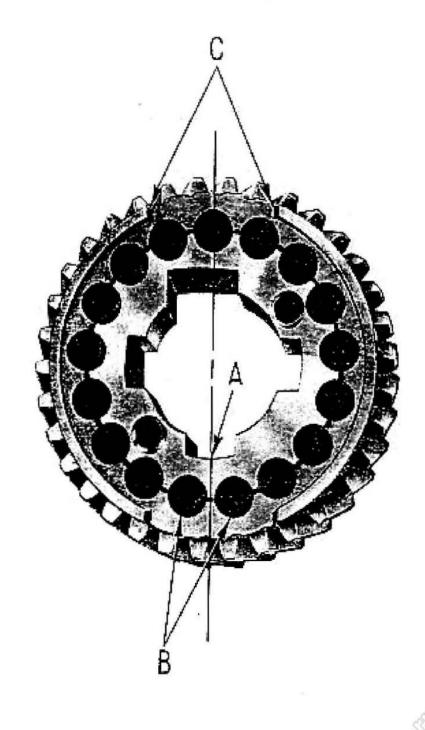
Come viene montato il corpo interno del pignone elastico motore.
